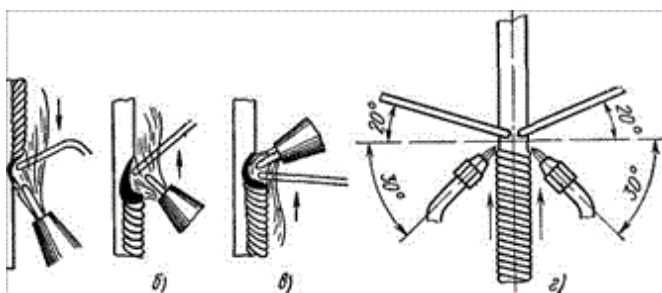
Сварка вертикальными швами: а - сверху вниз, б, в - снизу вверх, г - схема сварки двойным валиком
